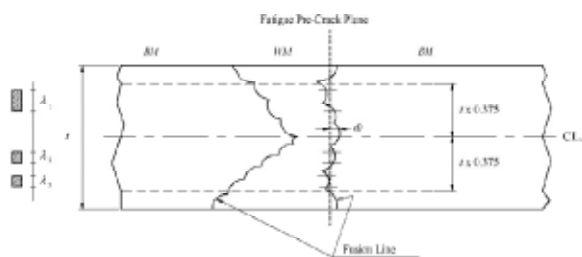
Sección transversal de la soldadura, que muestra la distancia " $df$ " desde el plano del crecimiento de la grieta a la línea de fusión
